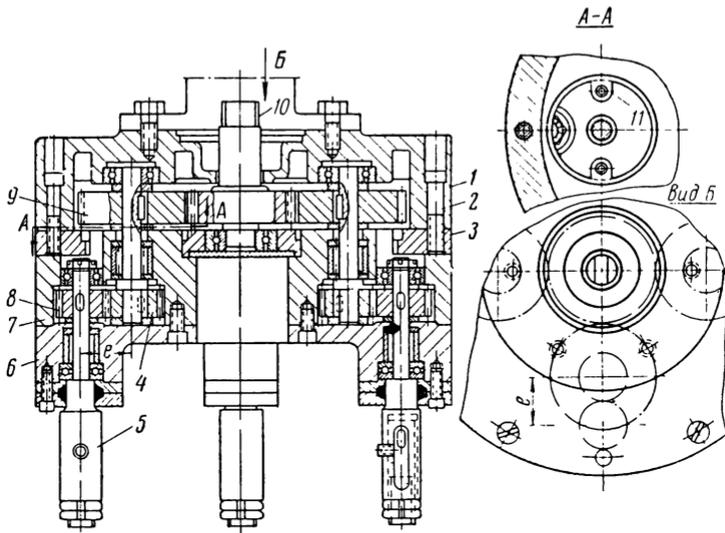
Многошпиндельная сверлильная головка для сверления отверстий, расположенных по окружности
